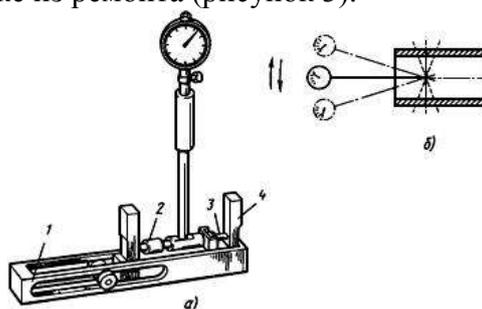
Индикаторное приспособление для измерения радиального зазора в подшипниках.
